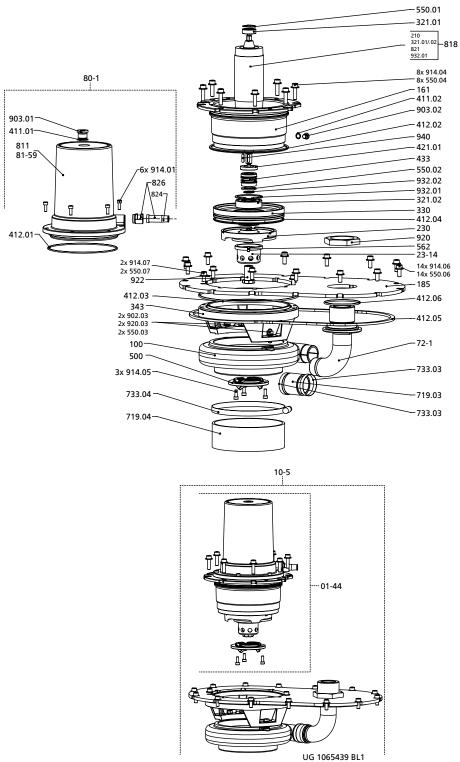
Деталировочный чертеж US100, UZS150 - ходовая часть
